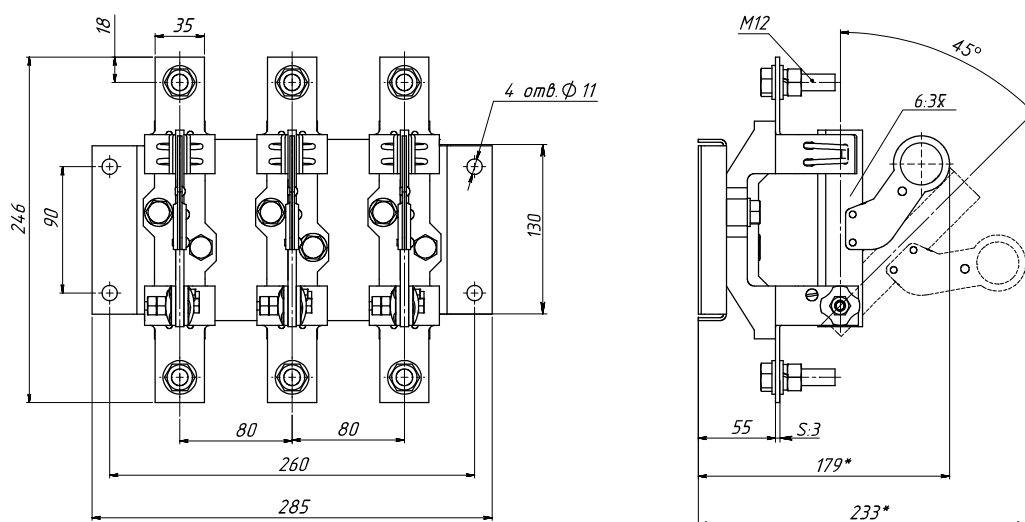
Разъединитель P63 с пополюсным оперированием штангой ШО-1, на номинальный ток 630 А
